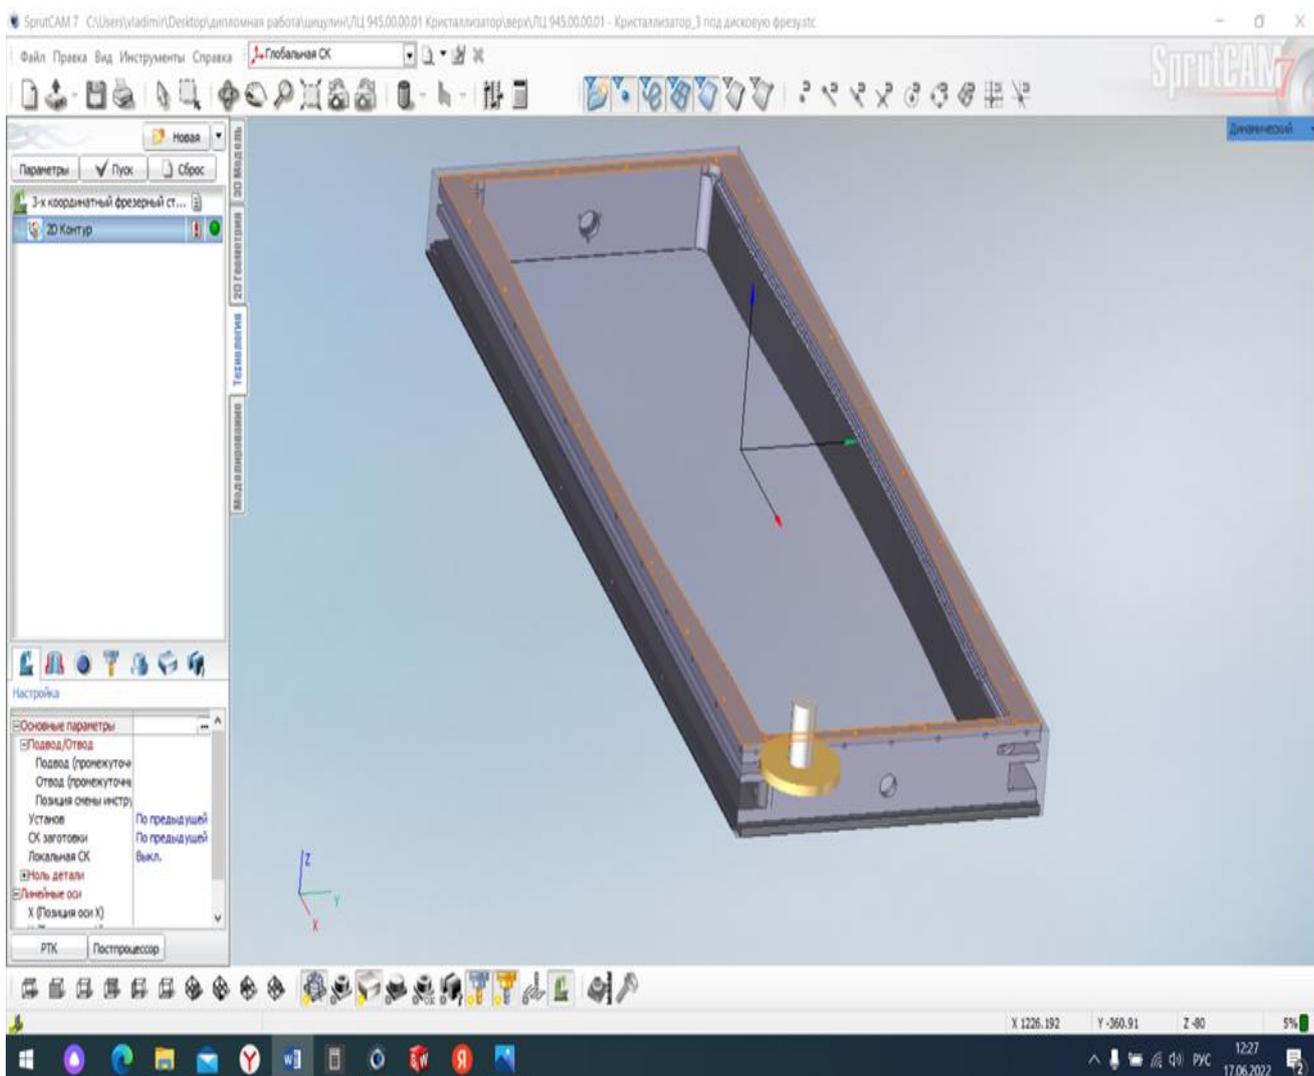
Обработка дисковой фрезой на оправке боковых контуров.
